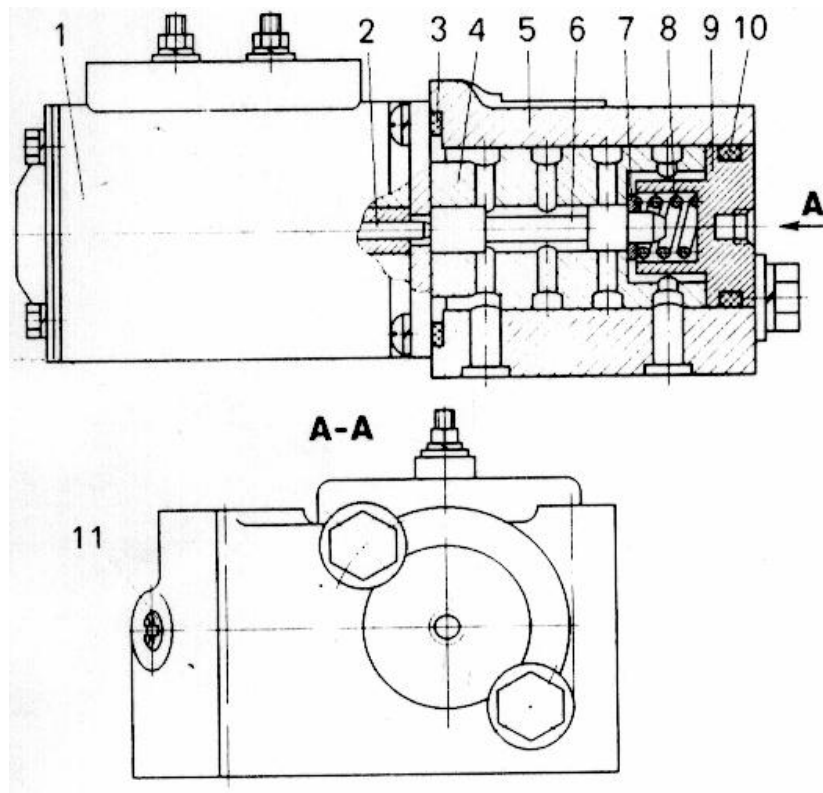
Механизм привода управления тормозом-замедлителем: 1 – электромагнит; 2 – толкатель; 3, 10 – уплотнительные кольца; 4 – гильза пилота; 5 – корпус; 6 – золотник пилота; 7 – шайба; 8 – пружина фиксатора; 9 – крышка; 11 – пробка
